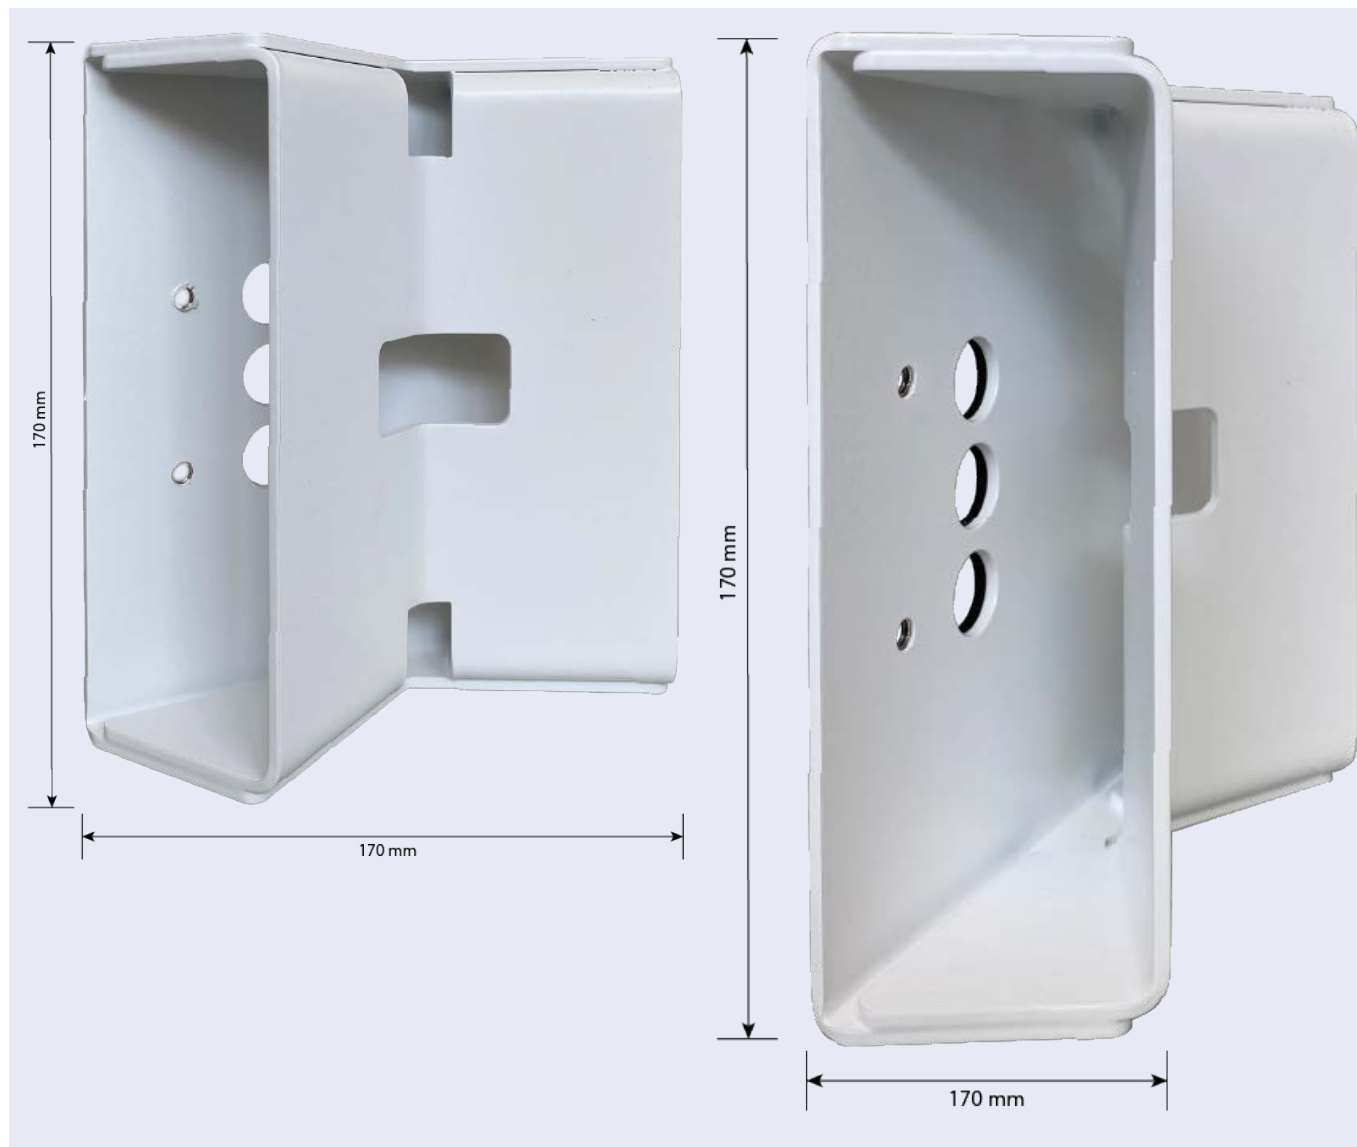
Dimensioni M73 montaggio su palo - vista posteriore
